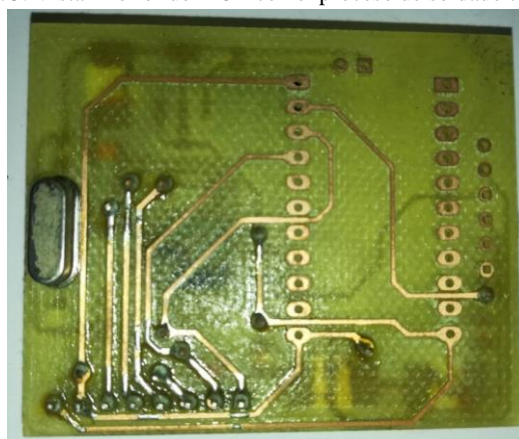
Vista inferior del PCB con el proceso de soldado terminado
